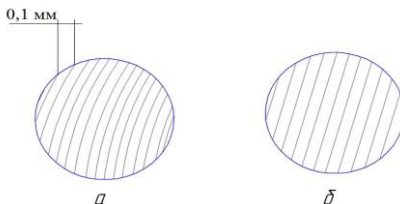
Схема определения длины режущей кромки: а – для криволинейной режущей кромки; б – для прямолинейной режущей кромки
